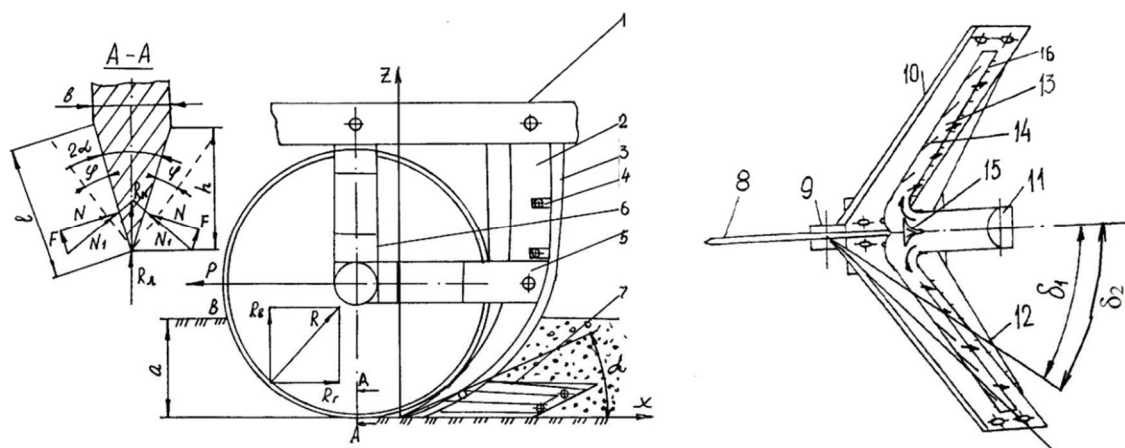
Комбинированный рабочий орган почвообрабатывающего орудия:
